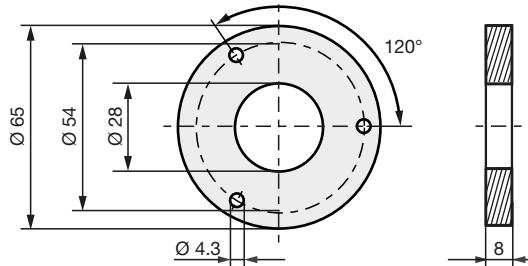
Accessori speciali BTL-P-1028-15R
